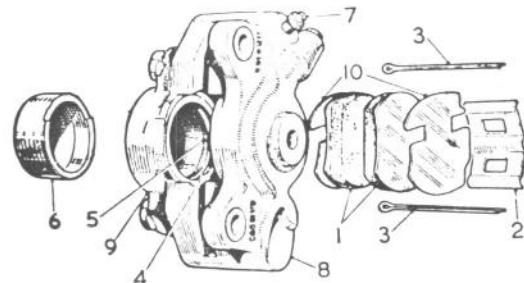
Despiece de un mecanismo de frenos de disco, del primer modelo.
